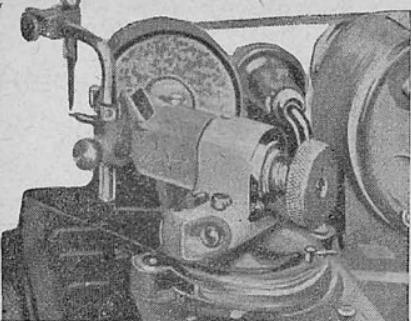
Проверка зазора шарошки при помощи специального калибра
